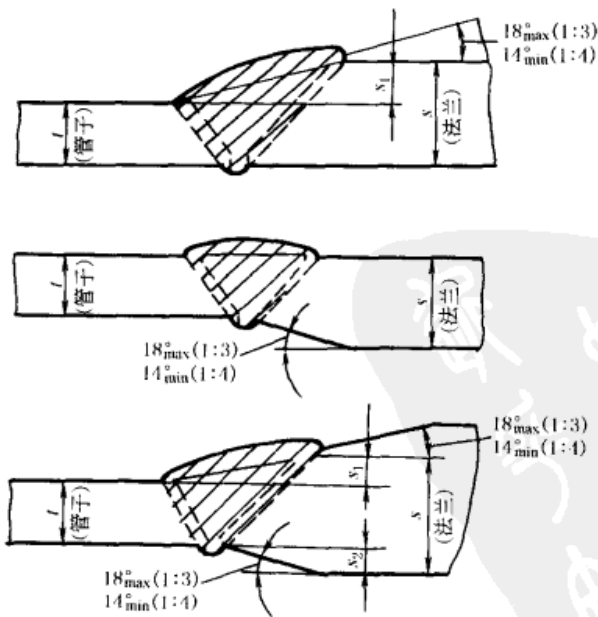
对焊法兰与钢管连接的焊接坡口型式和尺寸
